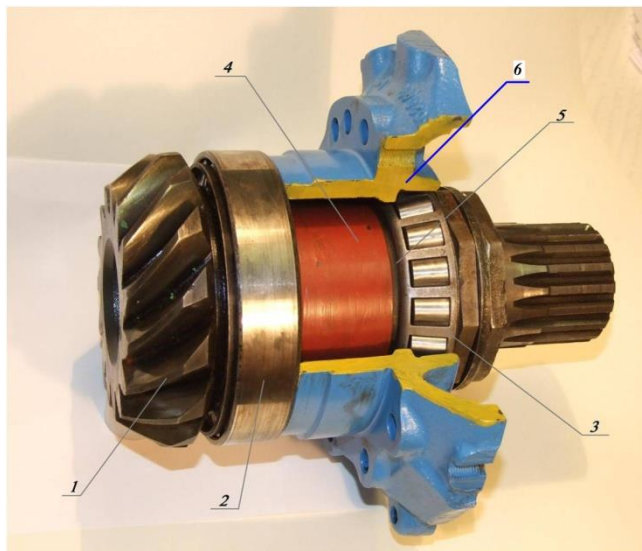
Подшипниковый узел редуктора заднего моста грузового автомобиля (1 – ведущая шестерня; 2 – подшипник ведущей шестерни; 3 – внутреннее кольцо подшипника; 4 – распорная втулка; 5 – компенсатор; 6 – корпус)
